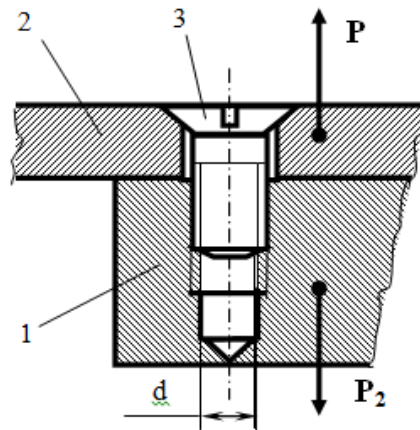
Схема сил у з'єднанні: 1 – корпус циліндра; 2 – станина пристрою; 3 - гвинт
